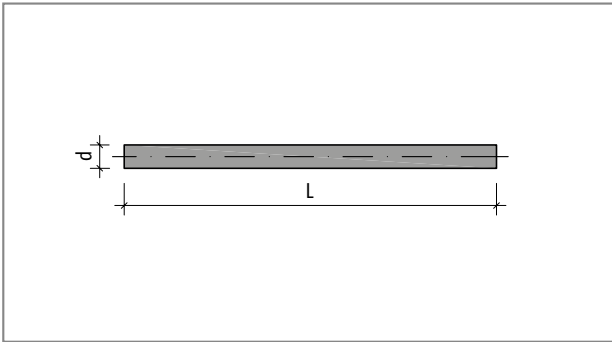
Schöck Dorn type LD Part A4, LD Part Zn : Dimensions du goujon
